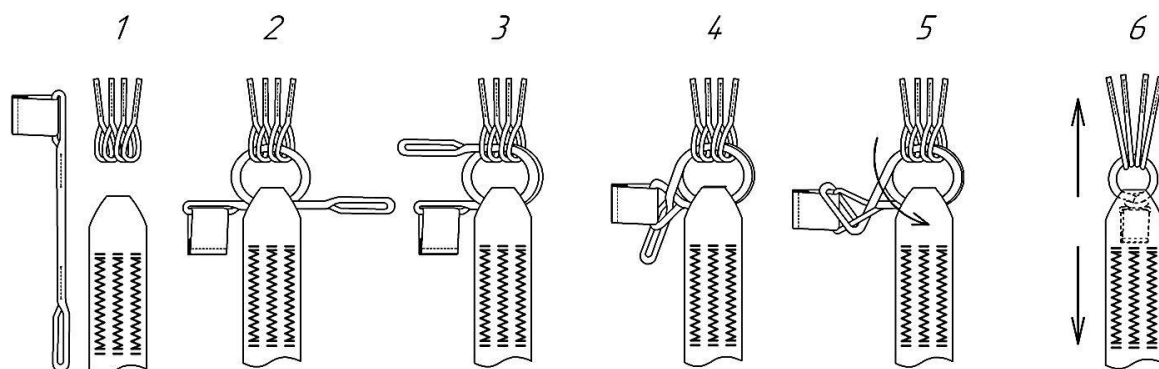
Монтаж строп мягкими соединительными звеньями
